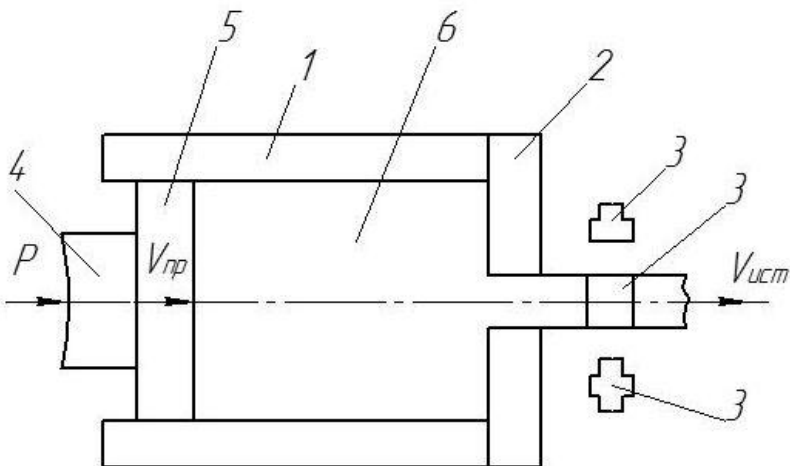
Схема прессования: 1 - контейнер; 2 - матрица; 3 - прессуемый профиль; 4 - пресс-штампель; 5 – пресс-шайба; 6 - заготовка.
